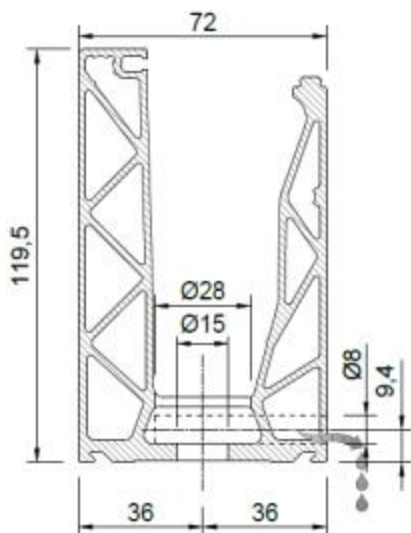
section transversale du profilé DF88MS.60 avec indication de perçage pour drainage
